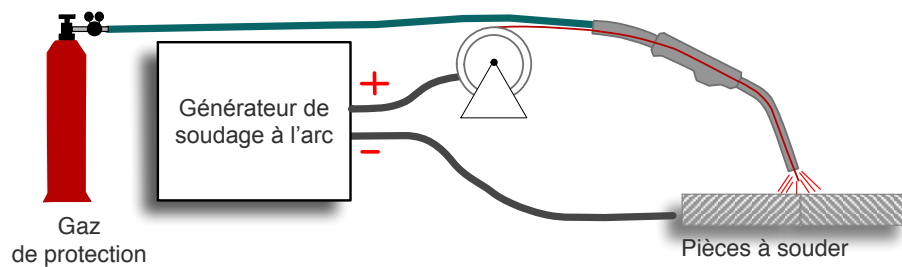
Schéma de principe du soudage MIG/MAG
